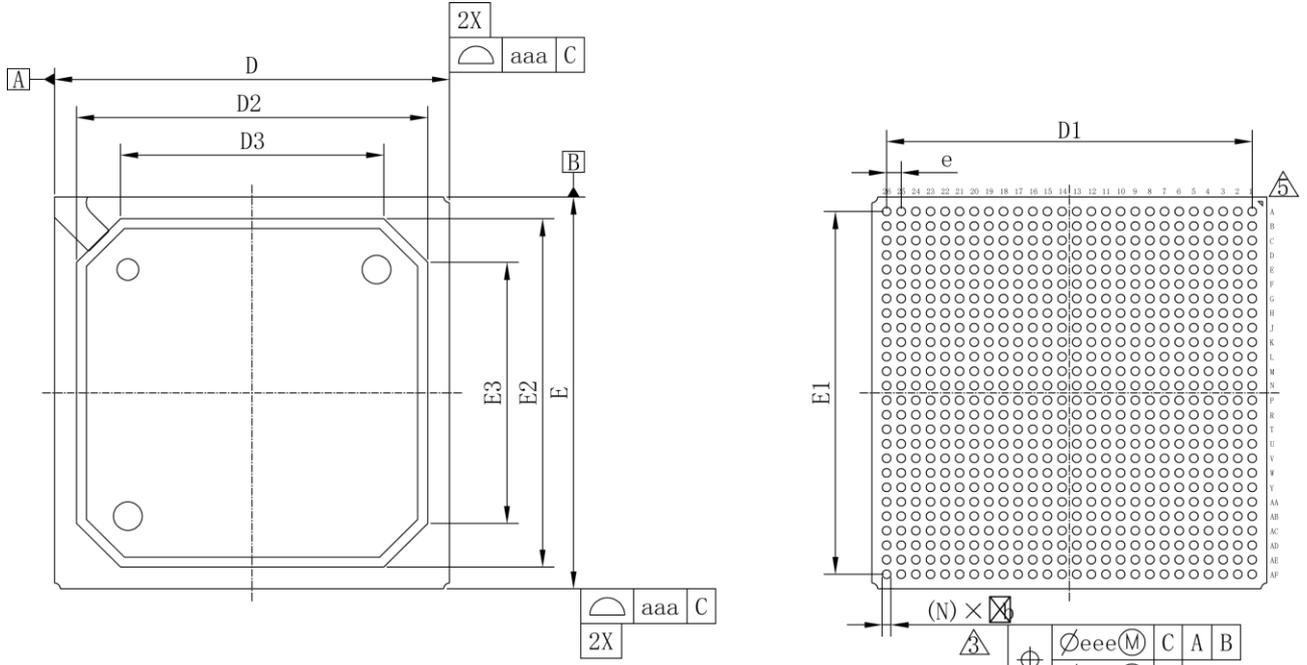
推荐 PCB Layout PG484F (GW5AT-138)
